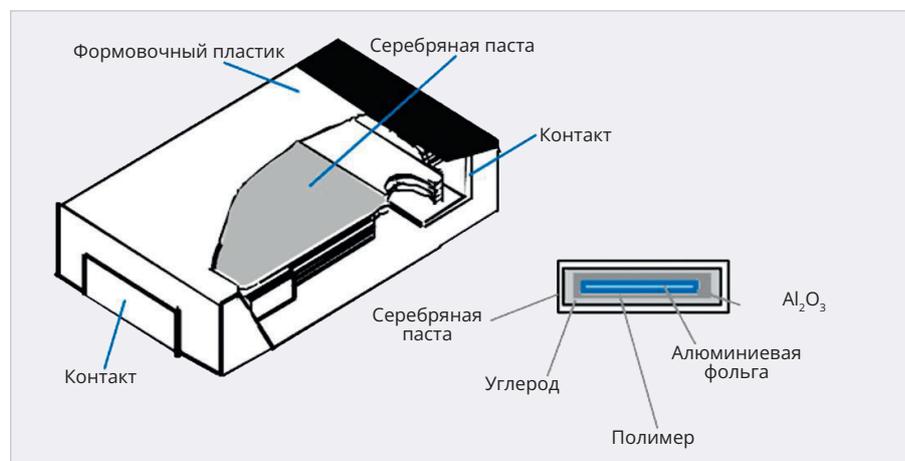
Многослойный полимерный алюминиевый конденсатор
